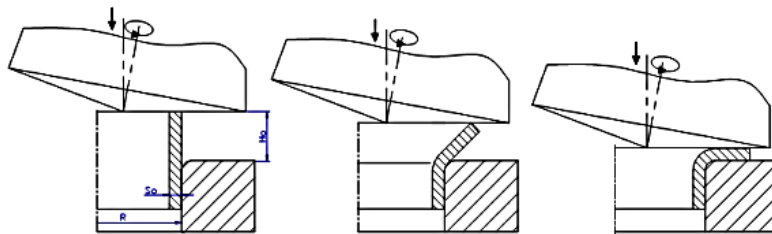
Відбортовка трубної заготовки розкочуванням зі зміщеним конічним валком
